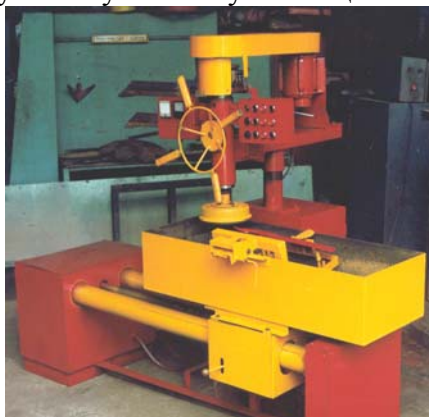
Установка для електроерозійної обробки 01.10.016А
